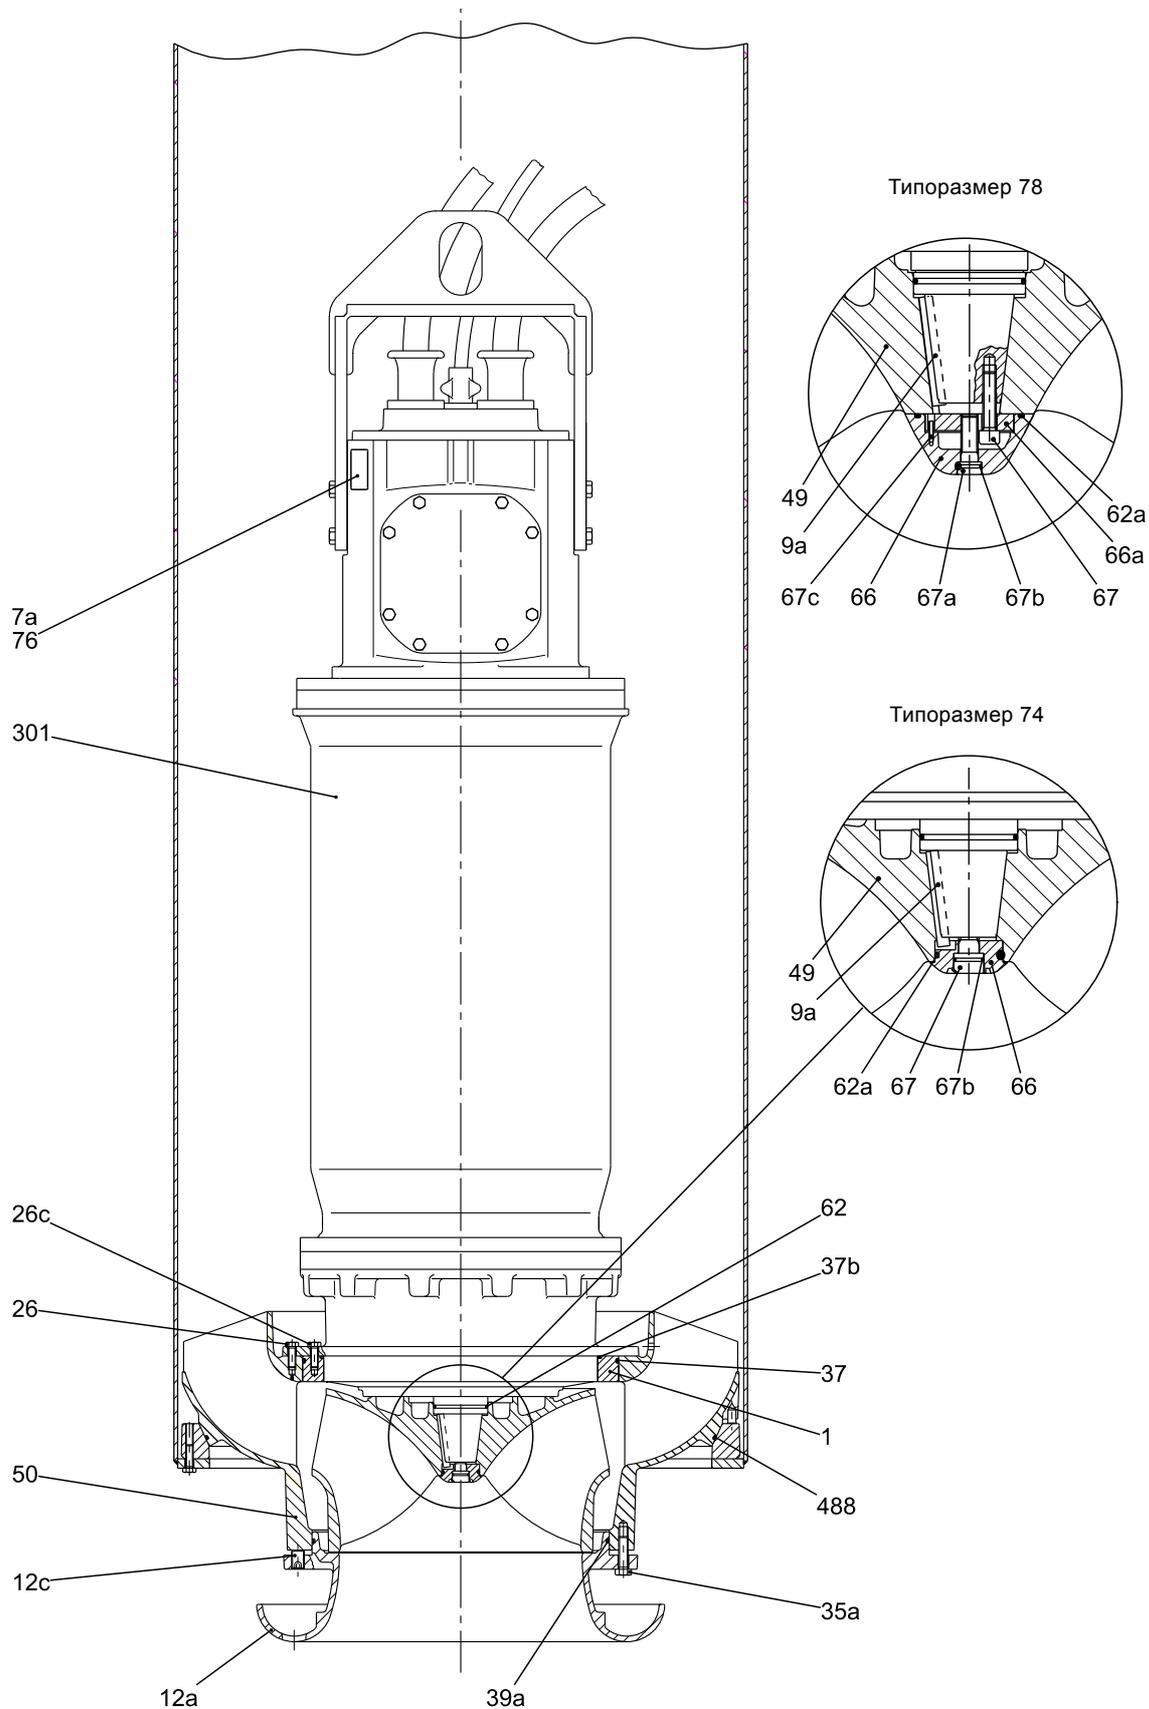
Типоразмеры 74 и 78 для установки в обсадной трубе (ST)
